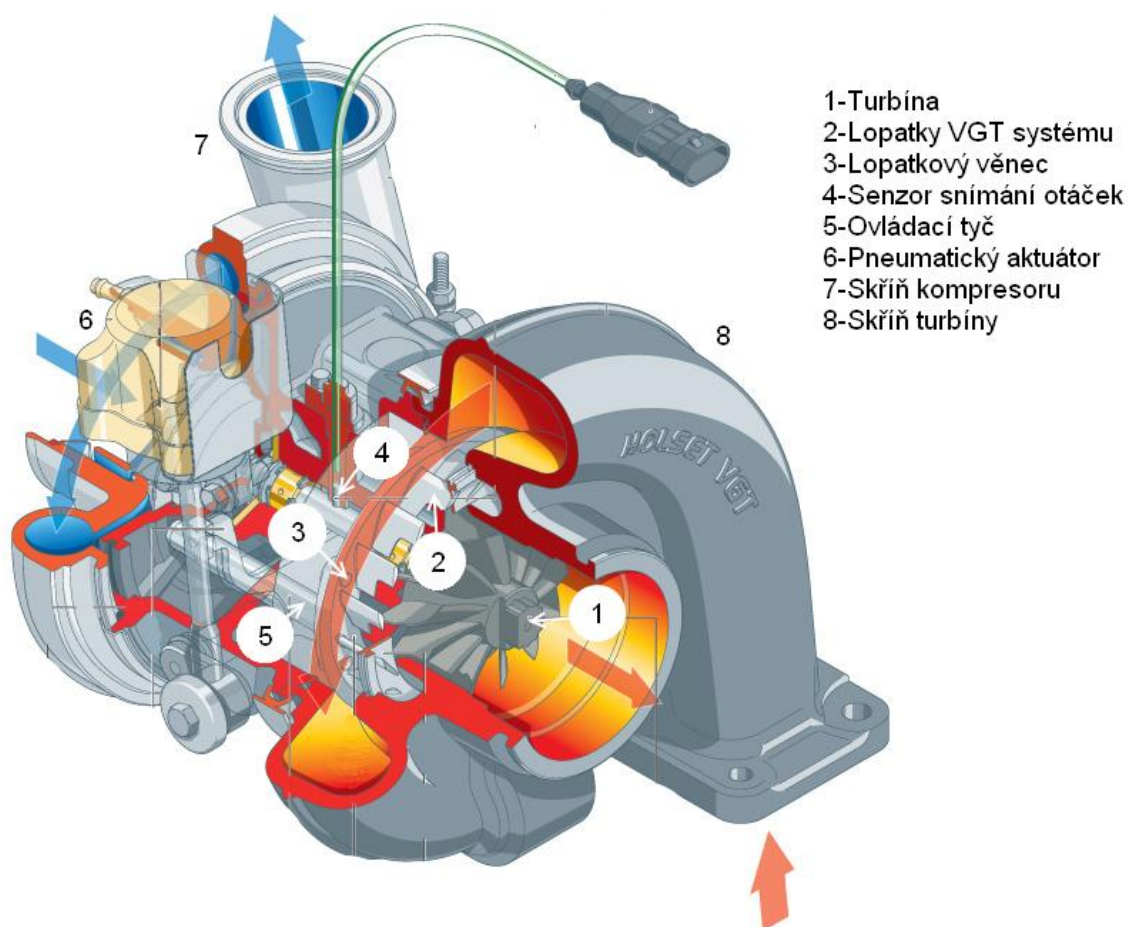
Řez turbodmychadlem s VGT technologií od fy Honeywell [21]
